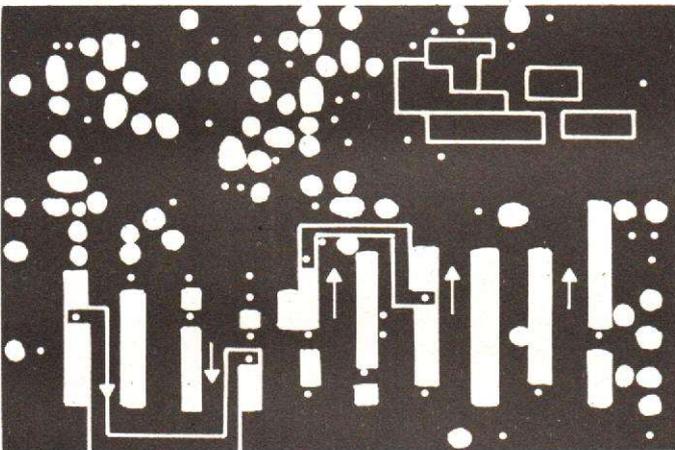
Le circuit imprimé (vue de dessous).
